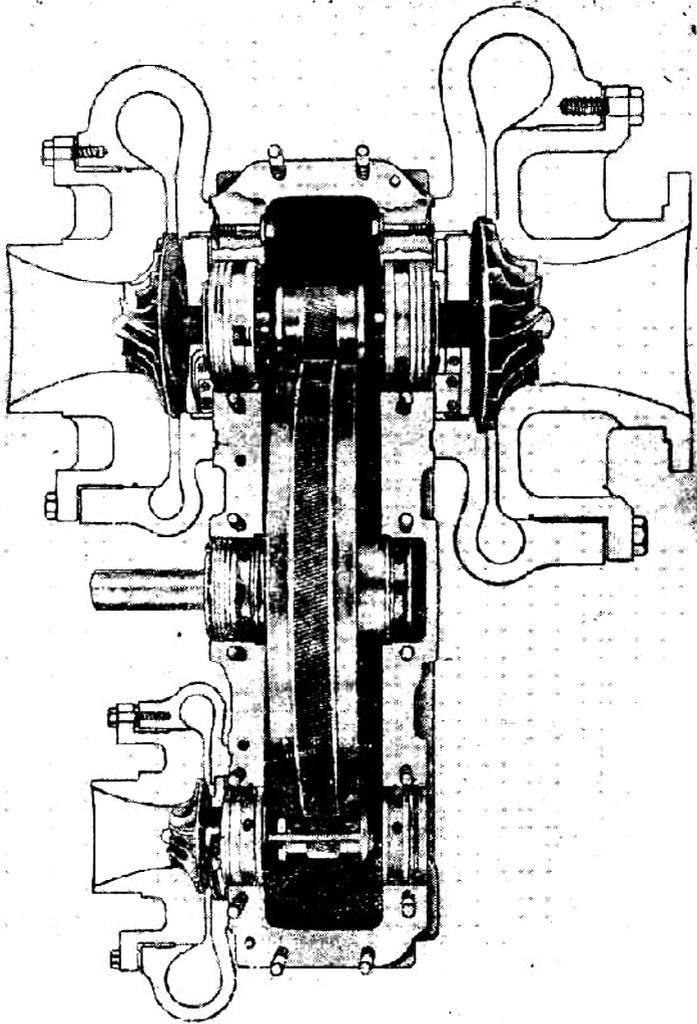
Внешний вид двухвального компрессора типа “DEMAG”
